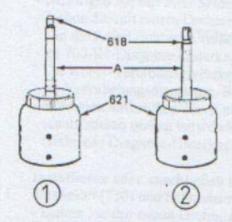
Turbinenwellen-O-Ring-Dichtung
